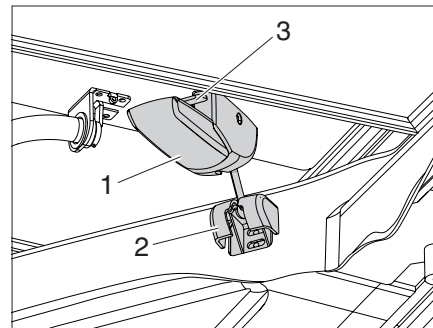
Lossa spaken genom att dra åt vänster eller höger
